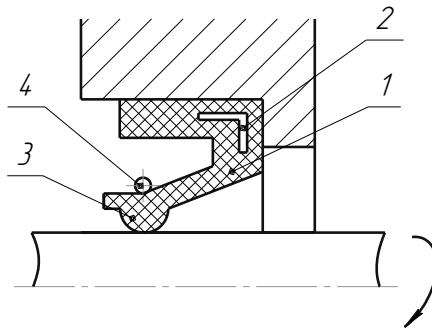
Манжета: 1 – корпус; 2 – металевий каркас;
